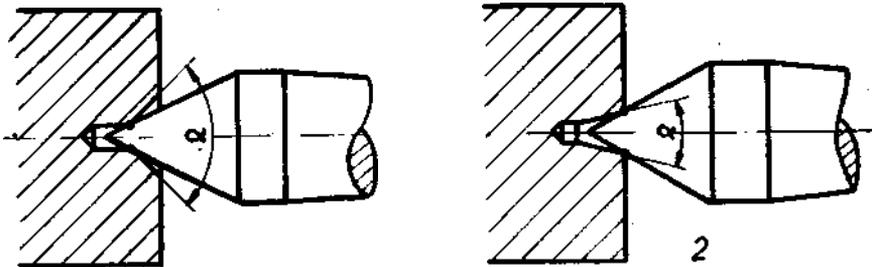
Disposiciones defectuosas del punto de centraje. A la izquierda, el ángulo α es mayor de 60° . A la derecha, el ángulo α es menor de 60° . En ambas disposiciones, la superficie de referencia pasa a ser línea de referencia.
